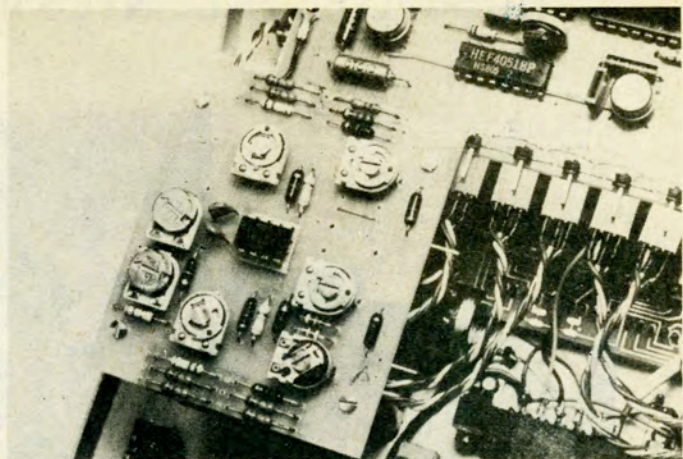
Photo F. - Gros plan sur la platine du manche ailerons-gaz. Noter les composants supprimés.
